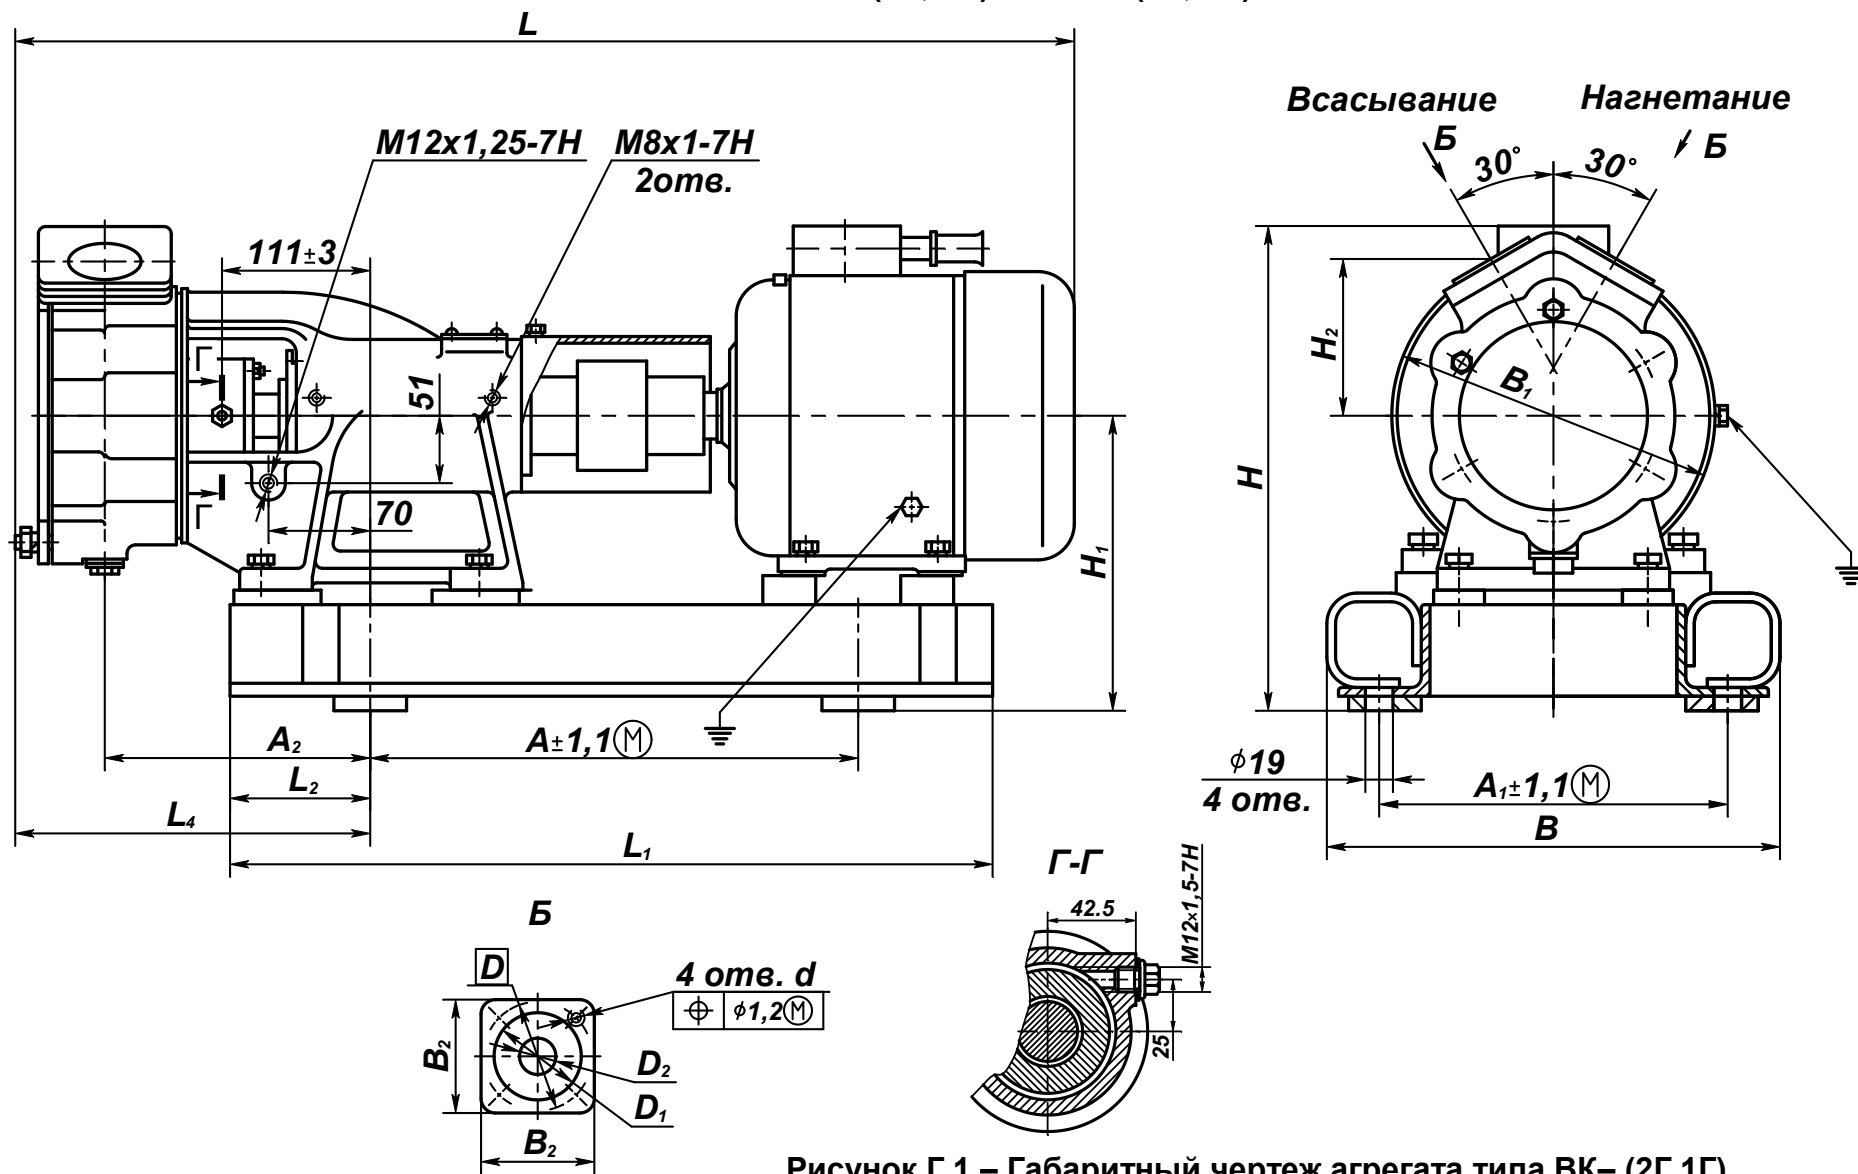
Габаритный чертеж агрегата типа ВК– (2Г,1Г)
